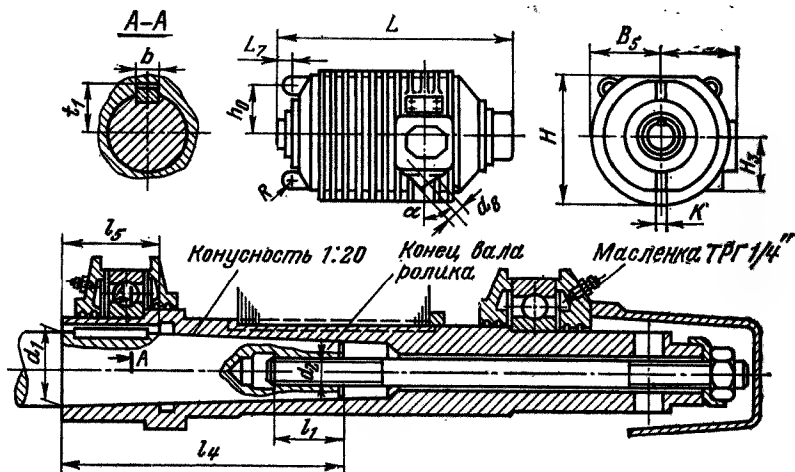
Габаритные и установочные размеры двигателей серии АРК 4—7-го габаритов.
